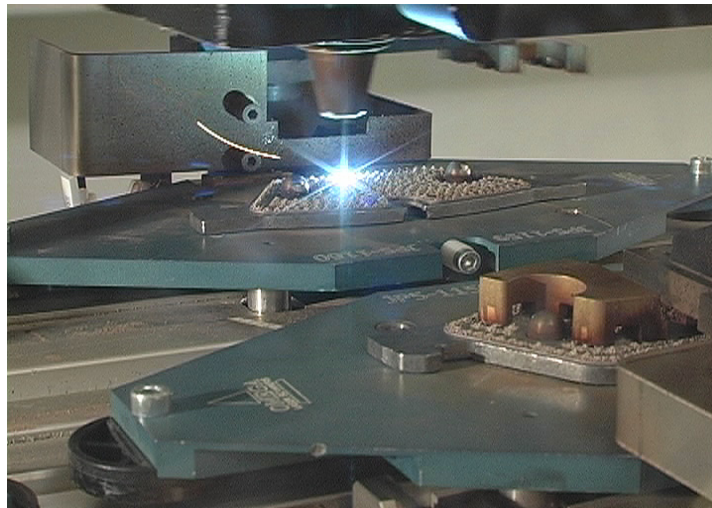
Beim Schweißen von Bremsbelagträgern
